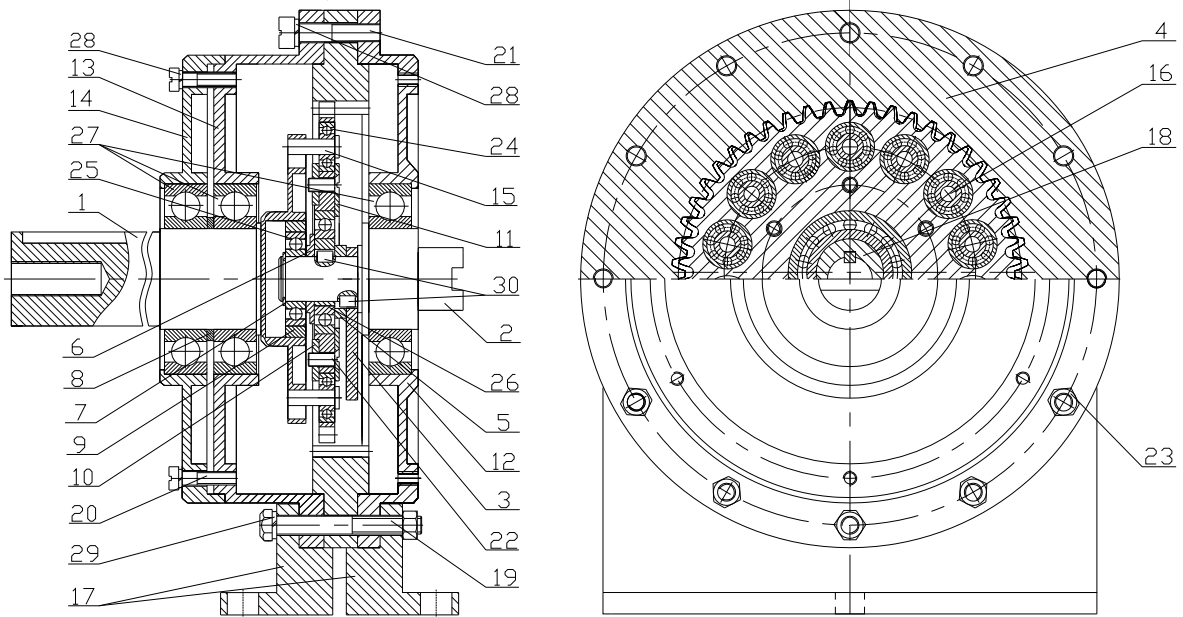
Чертеж планетарного эксцентрикового редуктора
